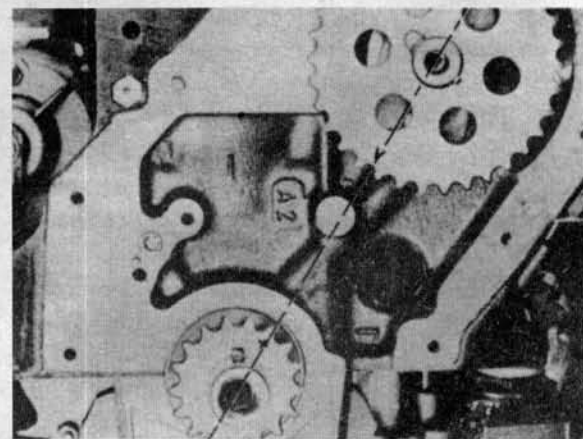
Установка шестерен привода механизма газораспределения при установке цепи в двигателе В13/В14
